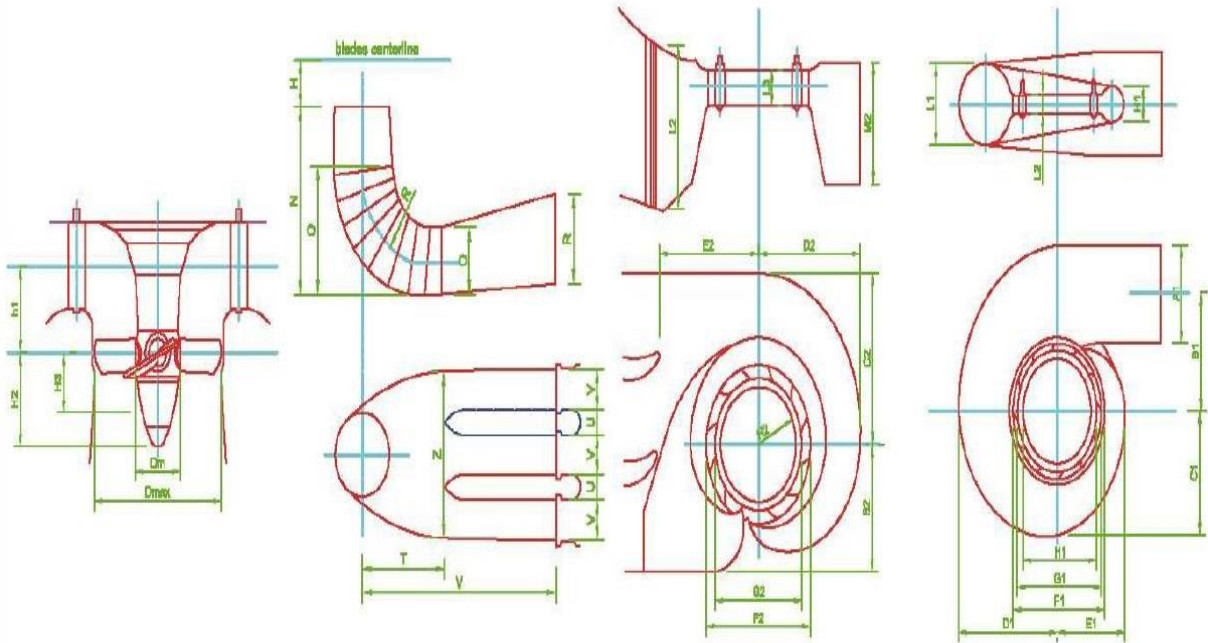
Dimensionamiento de turbinas Kaplan. (Zapico Gutiérrez, 2016)
